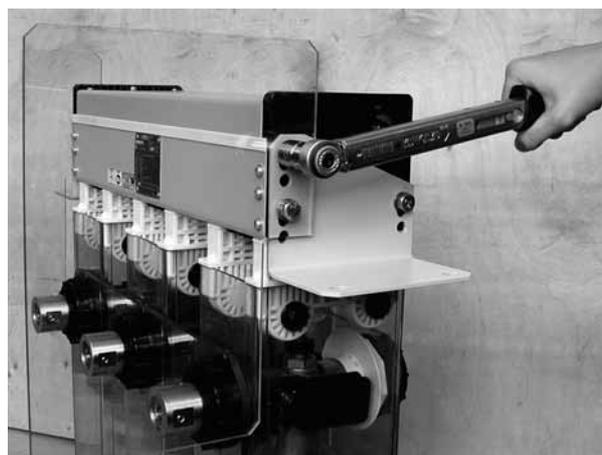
Установка балок крепления ВВ/TEL 10-20/1600
